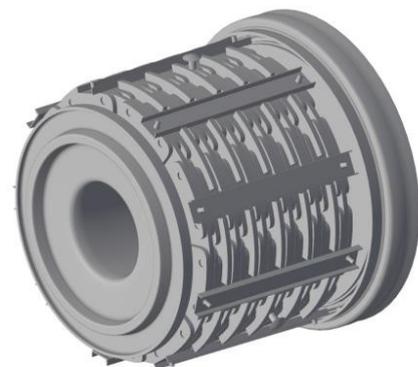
Пакет тормозных дисков на корпусе тормоза
